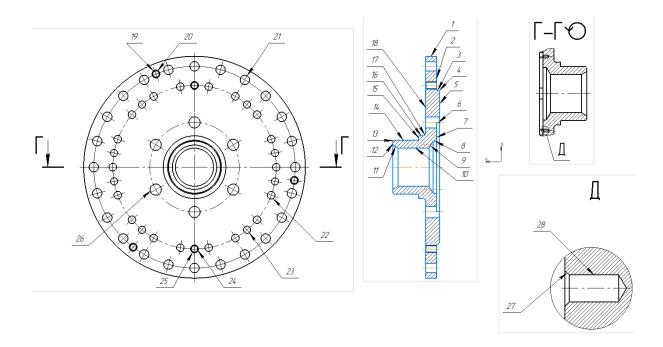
Чертеж детали "Фланец" с поверхностями
